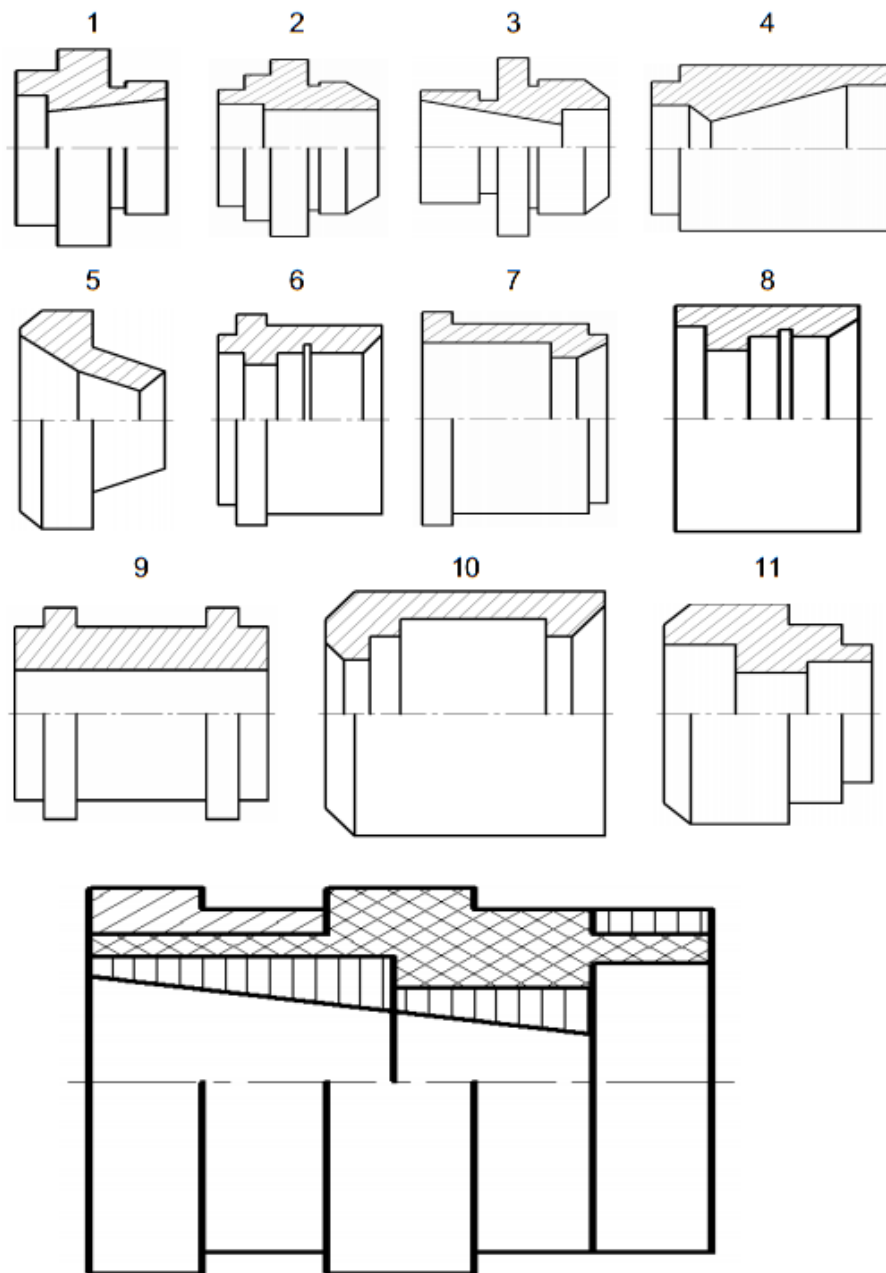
Схема створення комплексної деталі типу втулки
